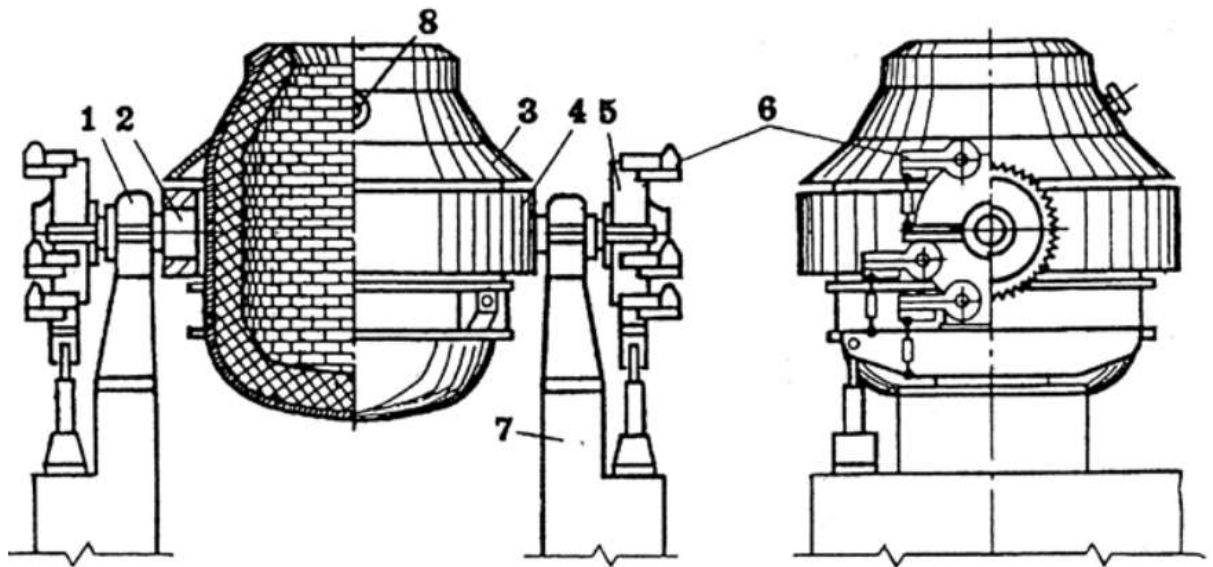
Схематичний вигляд кисневого конвертера: «1 – підшипник; 2 – цапфа; 3 – кожух; 4 – кільце; 5 – колесо; 6 – двигун; 7 – станина; 8 – виливний отвір» [1]
